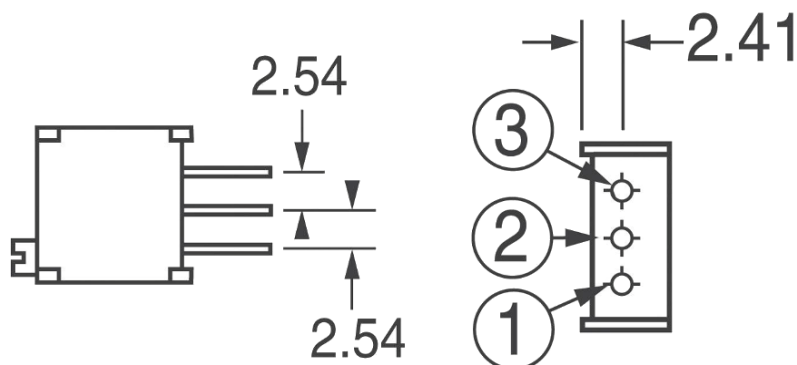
Габаритні розміри резистора 3296P-1-102LF
